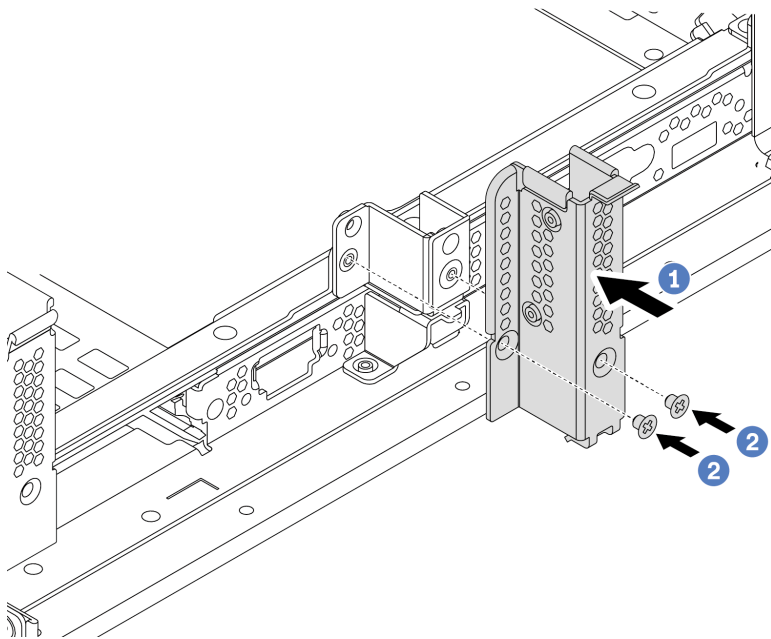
Installazione della staffa posteriore B1 per il montaggio a parete
